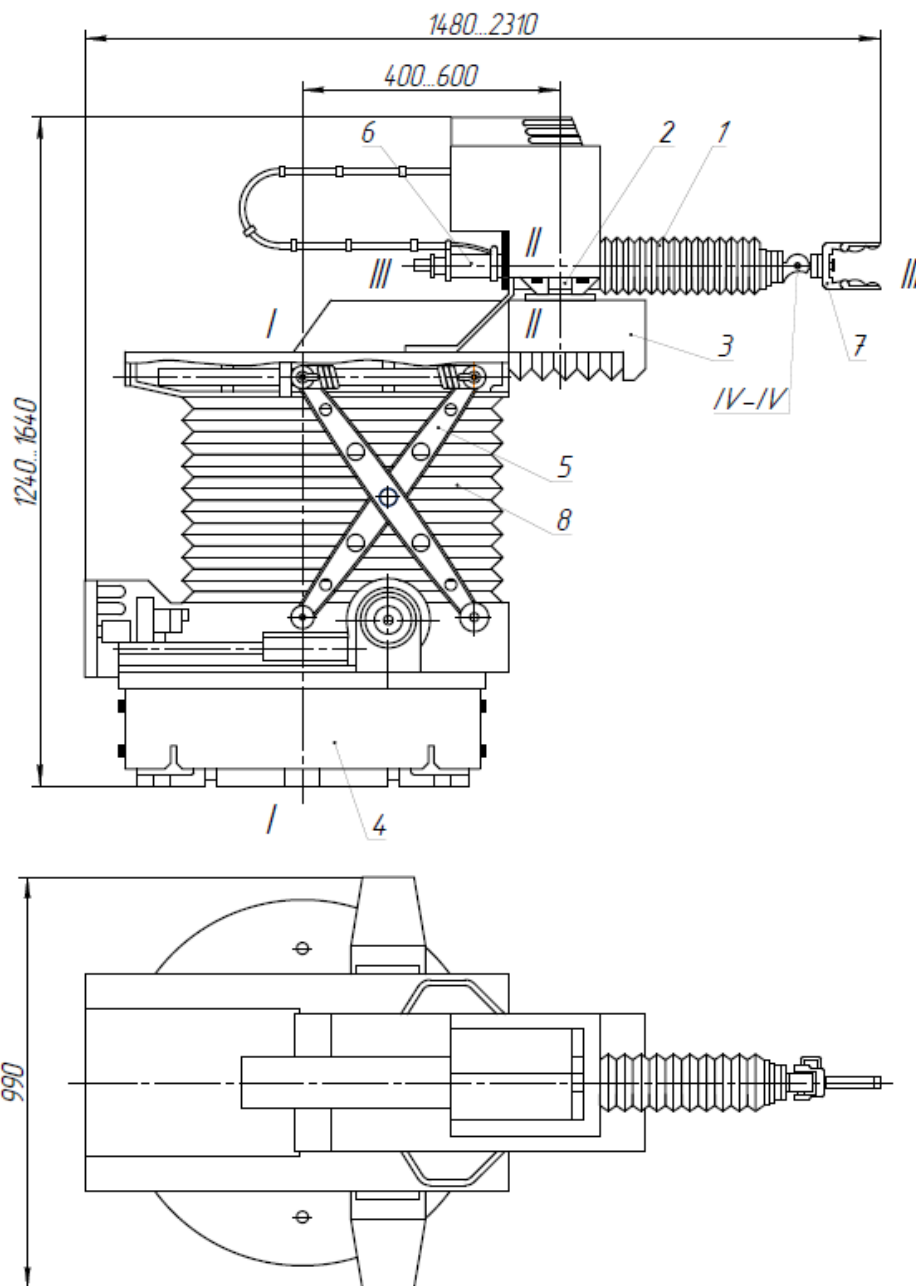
Багатоцільовий промисловий робот: 1 - механічна рука; 2 - механізм повороту; 3 - механізм висування; 4 - механізм повороту руки; 5 - механізм підйому руки; 6 - механізм обертання кисті руки; 7 - захват; 8 - огородження
